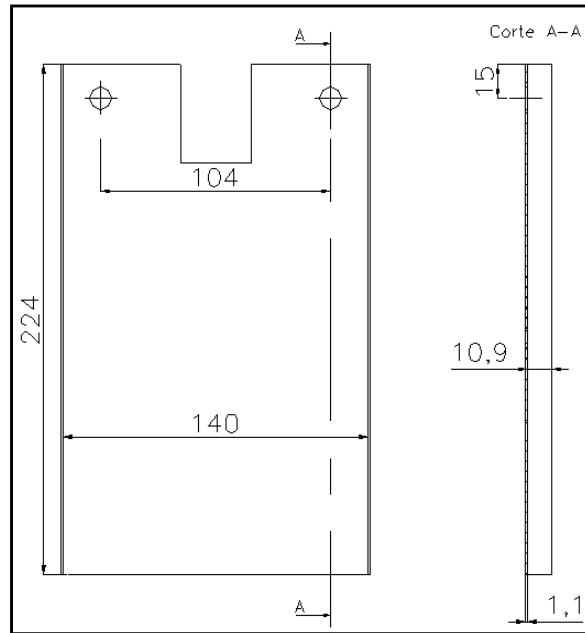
Dimensiones de la placa soporte para el motor a pasos
